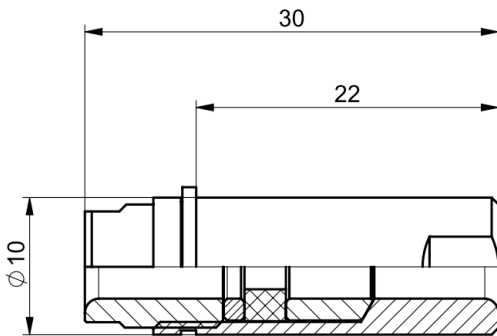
Adapter Typ 1700A37B (für Kabel ohne Kabelschutz)
